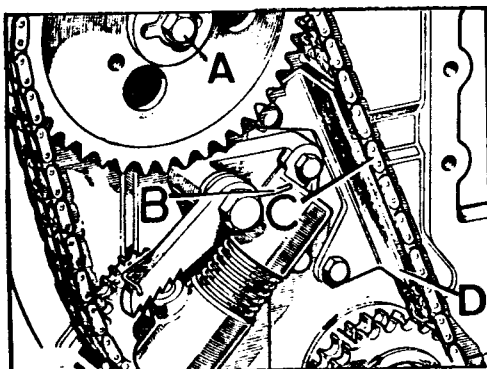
J Montaje tensor hidráulico, patín y fijación engranaje árbol de levas
